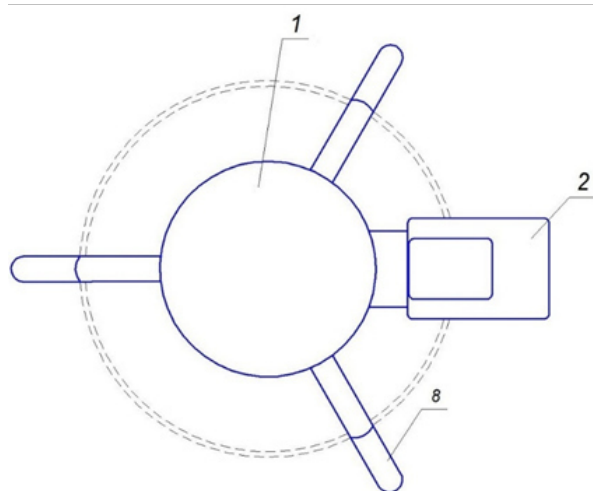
Мясорубка с вертикальным расположением шнека (вид сверху)
